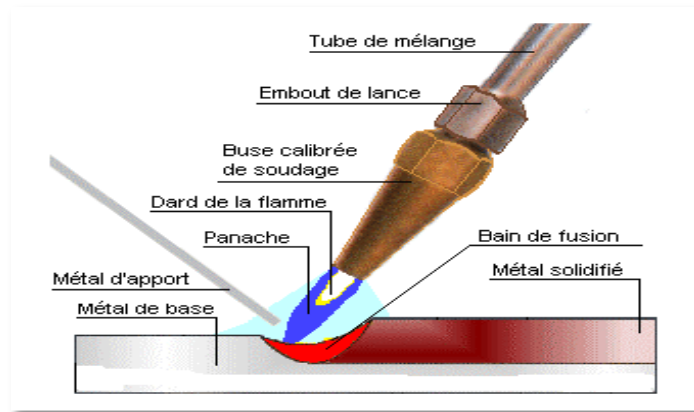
Principes de soudage par chalumeau [14].
